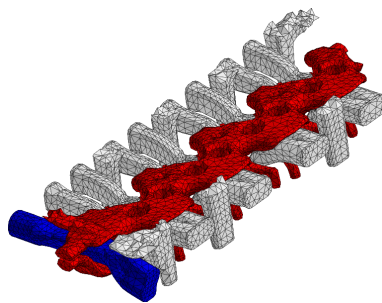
Zoom structural au niveau des noyaux internes
